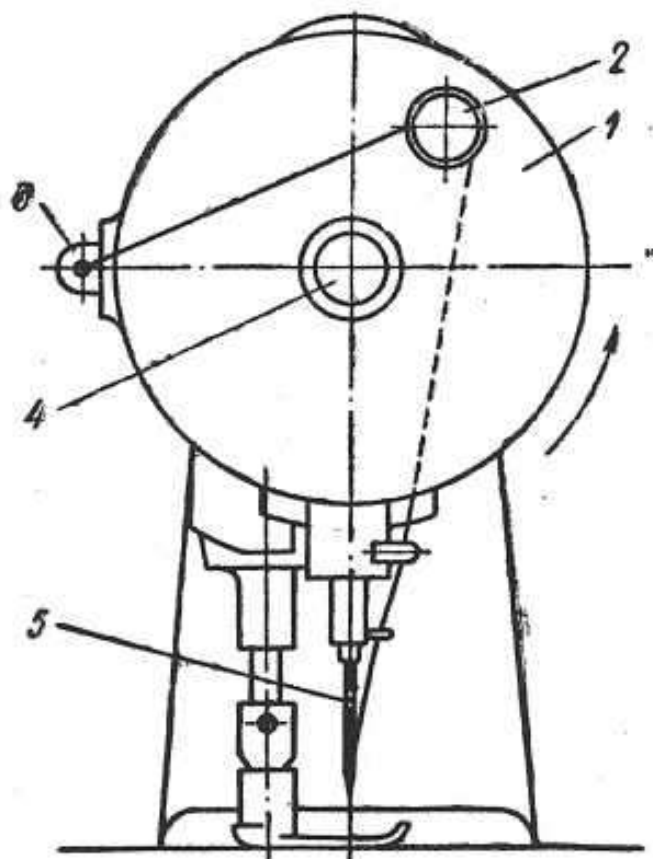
Ротаційний однопальцевий механізм ниткопритягувача
